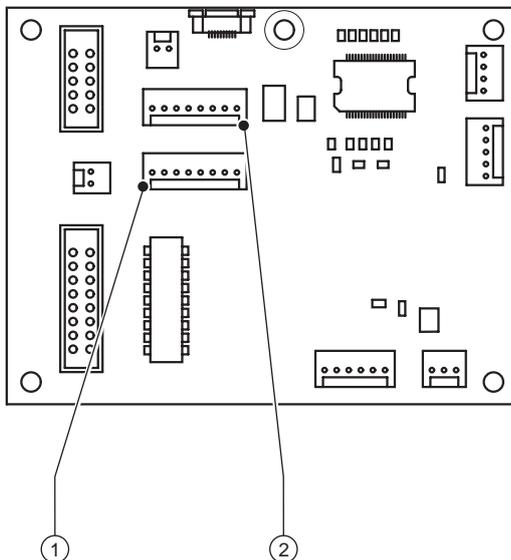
Kontaktierungsvarianten der Etikettenlichtschanke auf der Leiterplatte Sparantrieb
